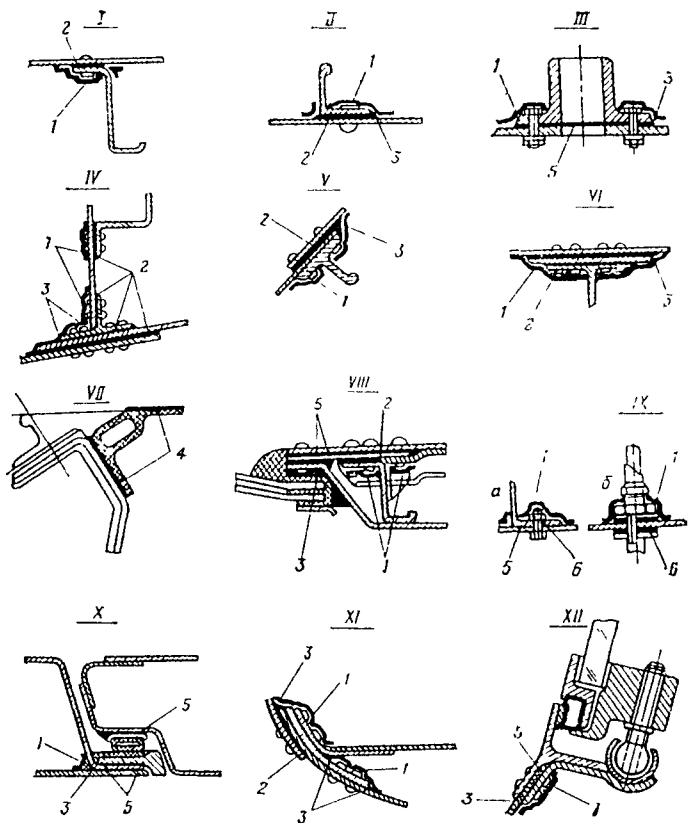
Герметизация типовых соединений фюзеляжа: I — стык шпангоута с обшивкой; II — стык стрингера с обшивкой; III — фланцевое соединение; IV — соединение шпангоута 40; V — продольный стык обшивки без подкладной ленты; VI — стык обшивки по шпангоуту 17 и 20; VII — стык центроплана; VIII — уплотнение в проеме окна; IXа — крепление кронштейнов; IXб — штуцерное соединение; X — уплотнение проемов дверей и люков; XI — соединение скуловой балки; XII — уплотнение форточек
